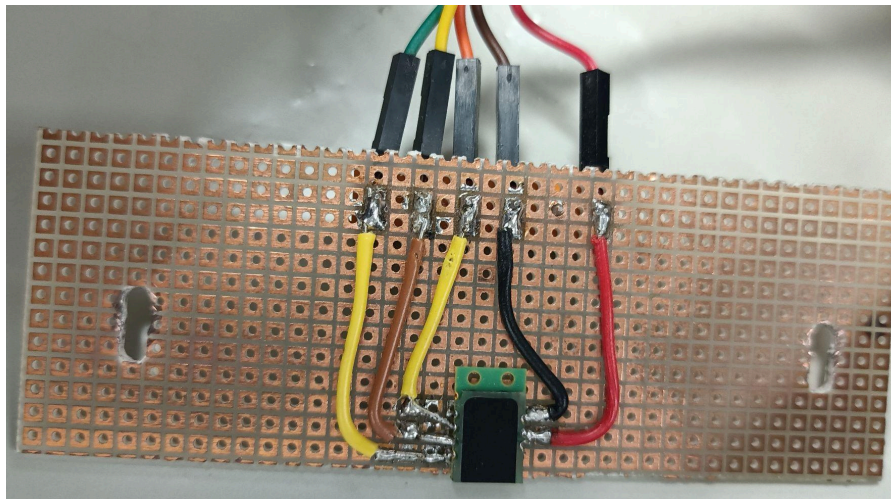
Lector de encoder magnético soldado en PCB
